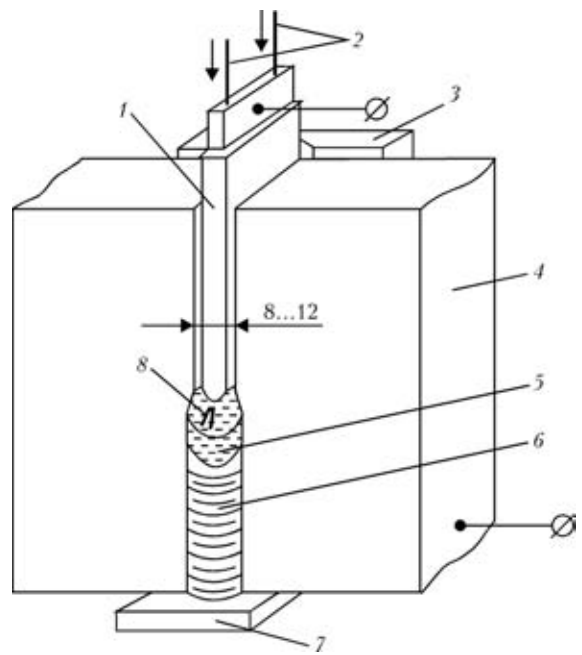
Схема электродуговой сварки закладным электродом: 1 — закладной электрод; 2 — присадочная проволока; 3 — формирующая накладка; 4 — свариваемое изделие; 5 — сварочная ванна; 6 — сварной шов; 7 — подкладка; 8 — дуга
